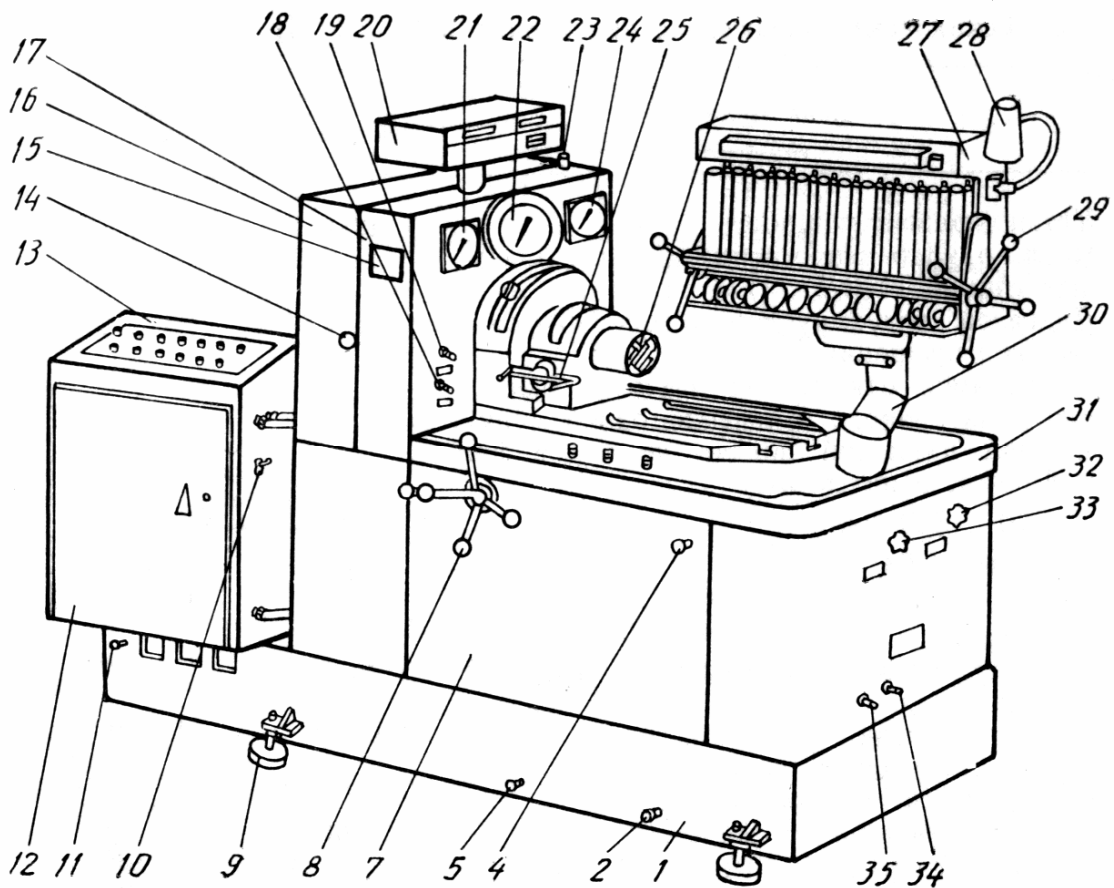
Стенд КИ-15711-01 для испытания и регулирования дизельной топливной аппаратуры:
